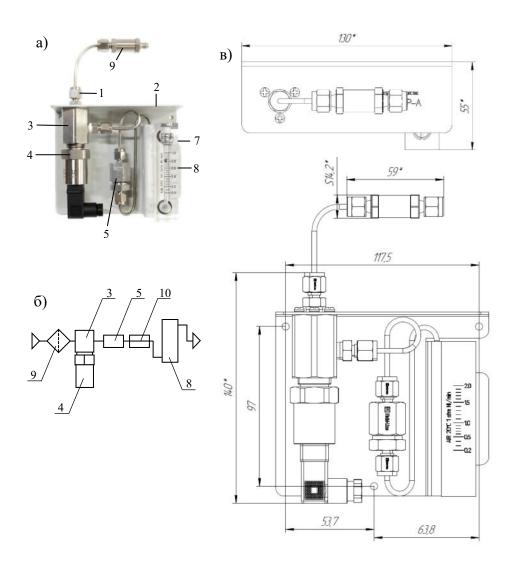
а) внешний вид, в) принципиальная пневматическая схема, б) габаритные размеры ПДВ-6-М-10-А-Р-Ф 1 – входной фитинг; 2 – основание для крепления; 3 – проточная камера; 4 – измерительный преобразователь влажности; 5 – дроссель; 7 – выходной фитинг; 8 – ротаметр; 9 – фильтр;
